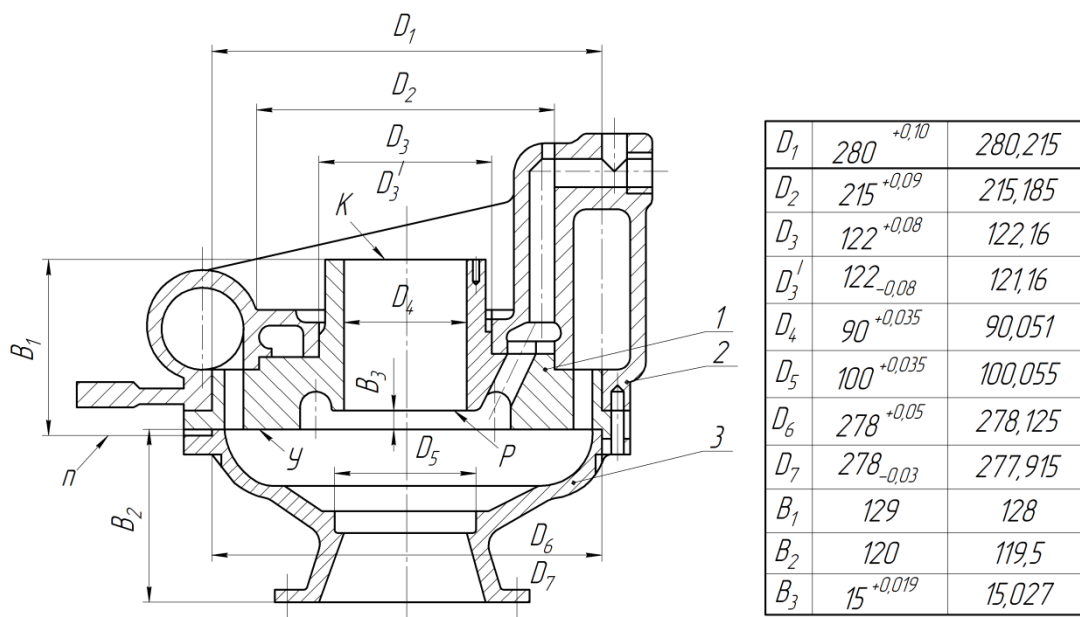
Корпус живлячого насоса: 1 — верхній корпус; 2 — улита; 3 — нижній
